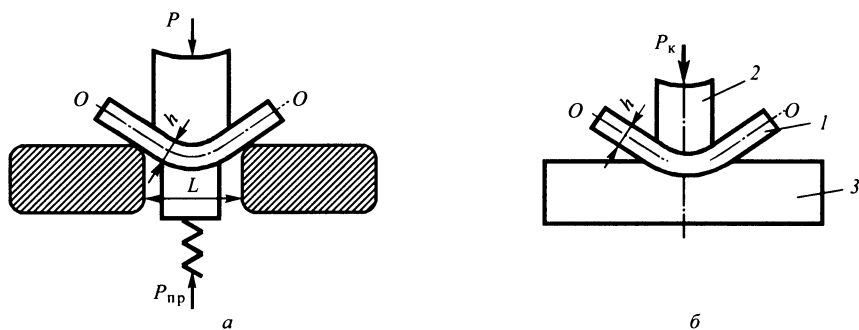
Схемы гибки с прижимом (а) и с калибровкой (б)
